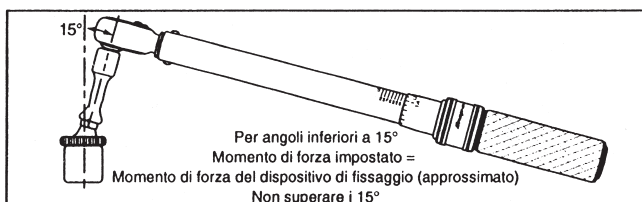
Il momento di forza del dispositivo di fissaggio è maggiore del momento di forza della trasmissione al quadrato della chiave torsionometrica.
